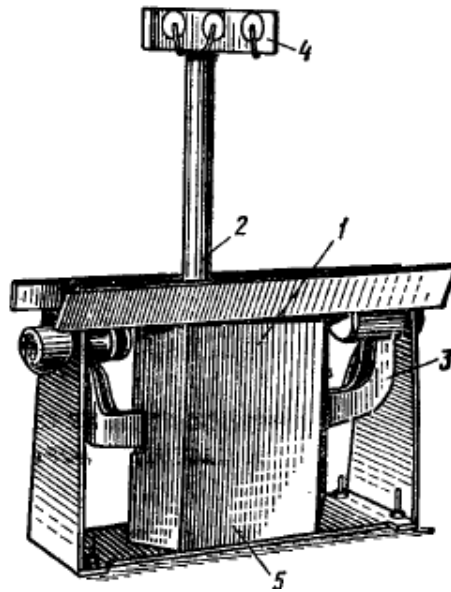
Кантувач 70-9864-1308 головок циліндрів двигунів А-01М и А-41: 1-корпус, 2- превмоциліндр, 3- коромисло, 4- пульт управління, 5- захисний кожух
